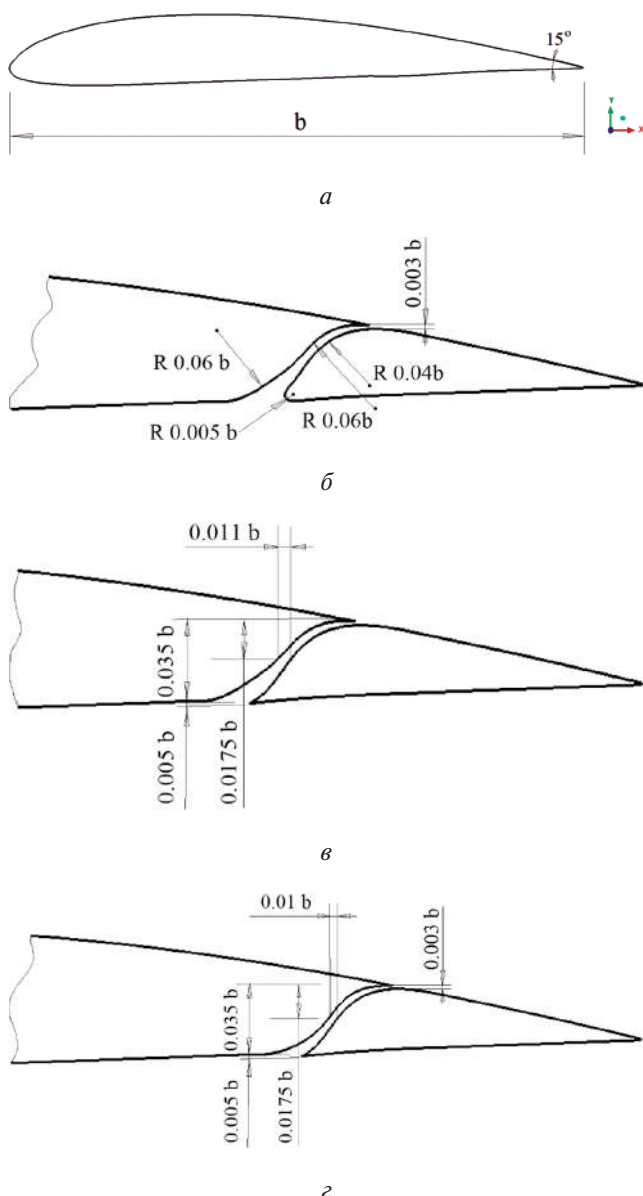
Общий вид профиля крыла и схема построения профилированного канала для выдува:
